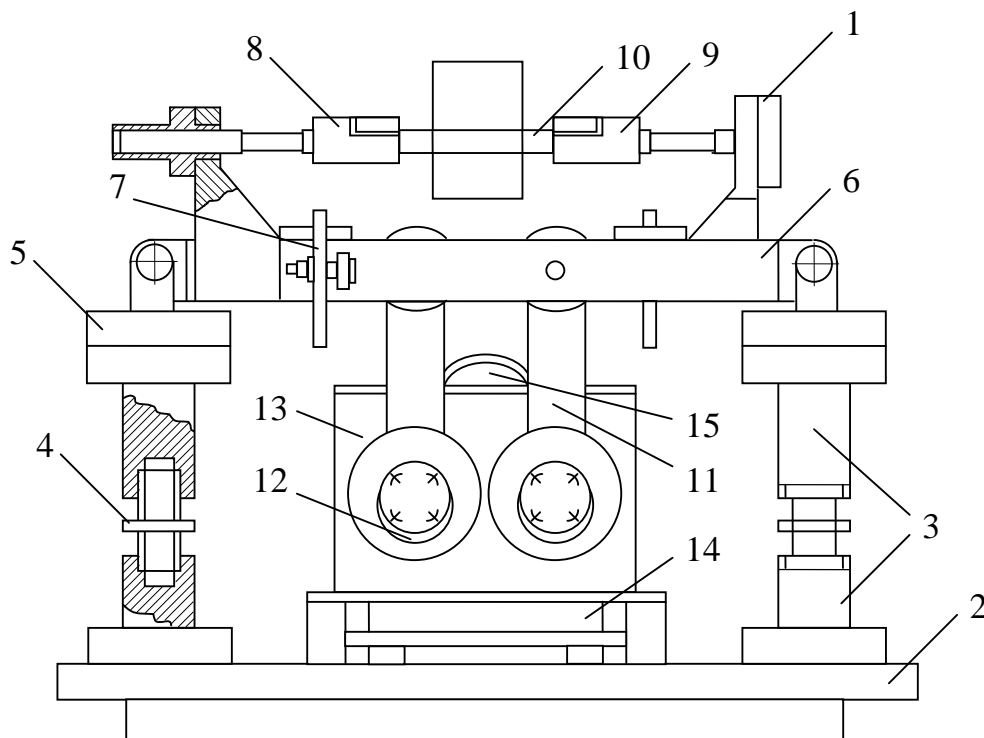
Конструкція випробувальної машини на чистий згин для дослідження втомного руйнування сталей
